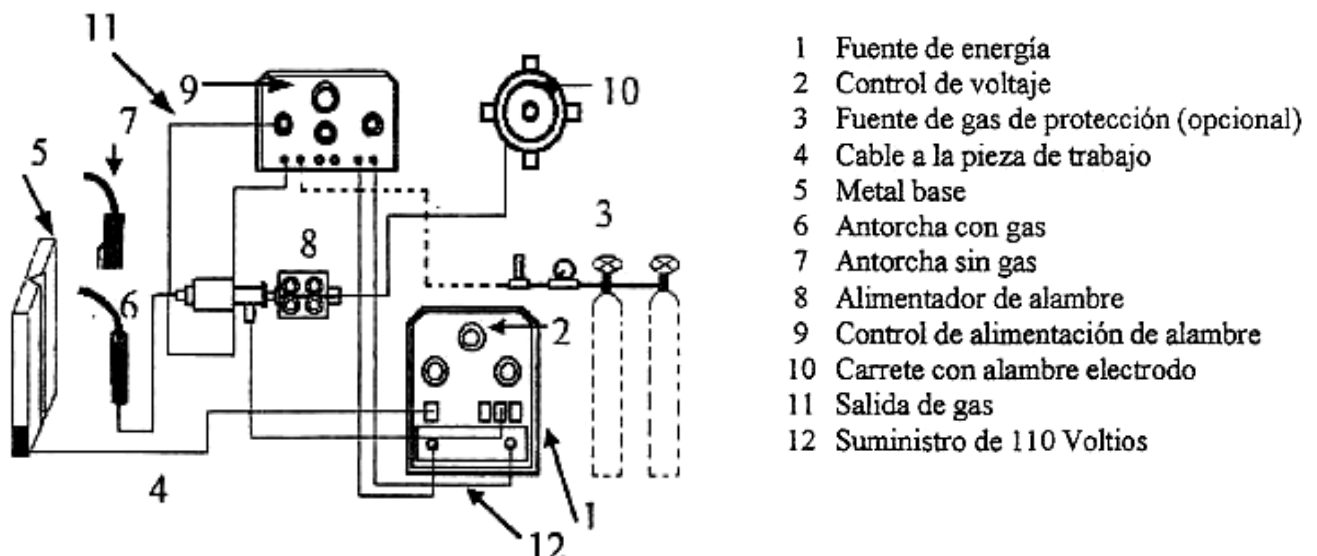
EQUIPO PARA EL PROCESO DE SOLDADURA POR ARCO CON ELECTRODO TUBULAR CON NÚCLEO DE FUNDENTE (FCAW)
